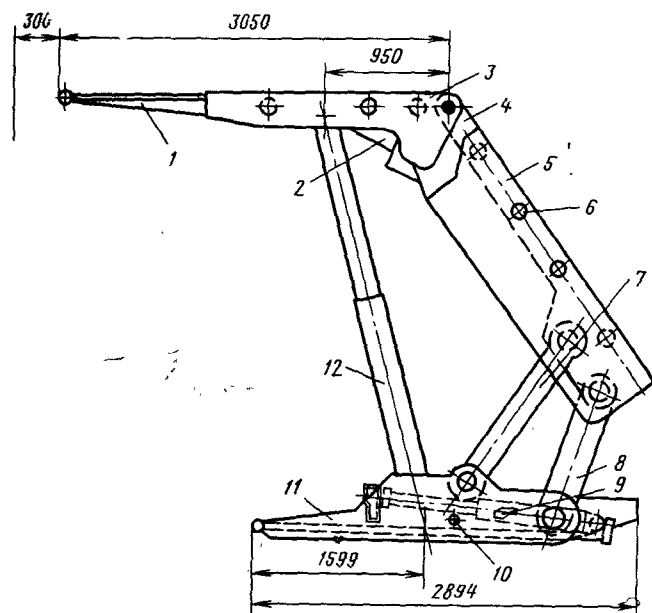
Механизированная крепь МХА-300/3,5 для пластов мощностью 1,3—3,2 м (КНР): 1 — консольная часть верхняка; 2 — гидродомкрат; 3 — верхняк; 4 — балка заднего перекрытия; 5 — боковое ограждение секции; 6 — отжимное шарнирное соединение боковин ограждения; 7, 8 — траверсы, соединяющие заднее ограждение с основанием секции крепи; 9 — гидродомкрат передвижения секции; 10 — шарнирное соединение; 11 — основание секции крепи; 12 — гидростойка
